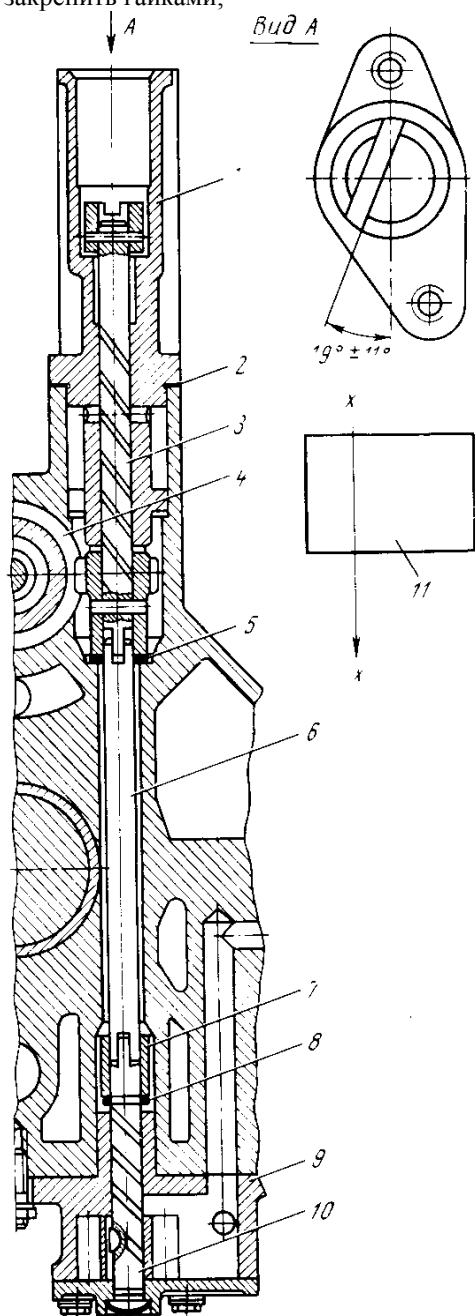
Привод распределителя зажигания: 1 — привод распределителя зажигания; 2 — прокладка; 3 — валик привода распределителя; 4 — ведущая шестерня привода распределителя; 5 — шайба; 6 — промежуточный валик привода масляного насоса; 7 — промежуточная втулка масляного насоса; 8 — стопорное кольцо; 9 — масляный насос; 10 — ведущий валик масляного насоса; 11 — масляный радиатор; x — x — ось коленчатого вала
